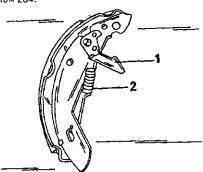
Правильное положение установочного рычага (1) и возвратной пружины (2) на тормозе Girling.
